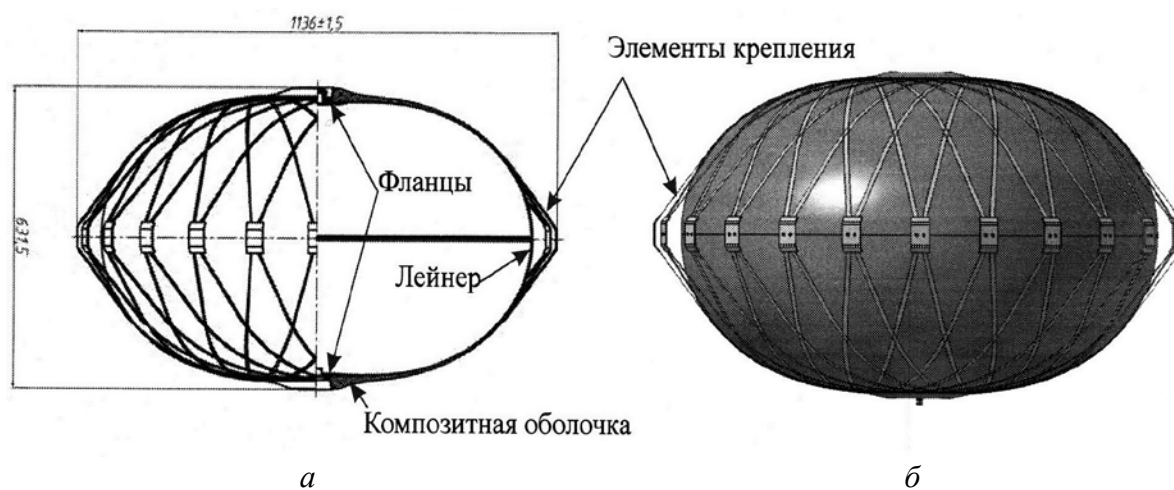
Конструкция (а) и общий вид (б) металлокомпозитного бака высокого давления
